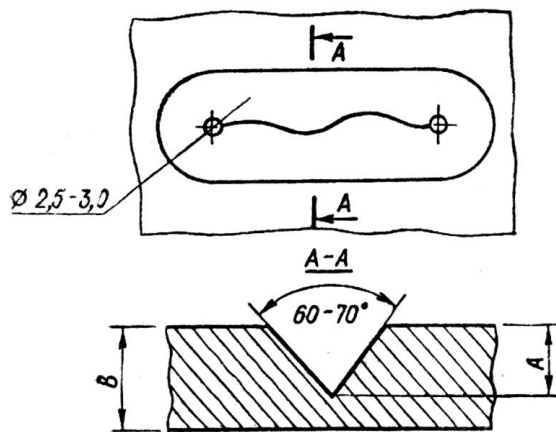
Обробка тріщини під зароблювання епоксидною композицією
